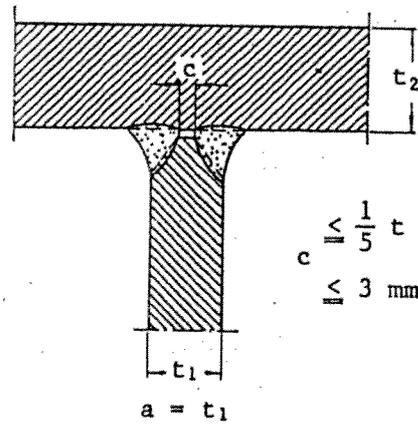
Soldadura en ángulo con preparación en K y penetración parcial
